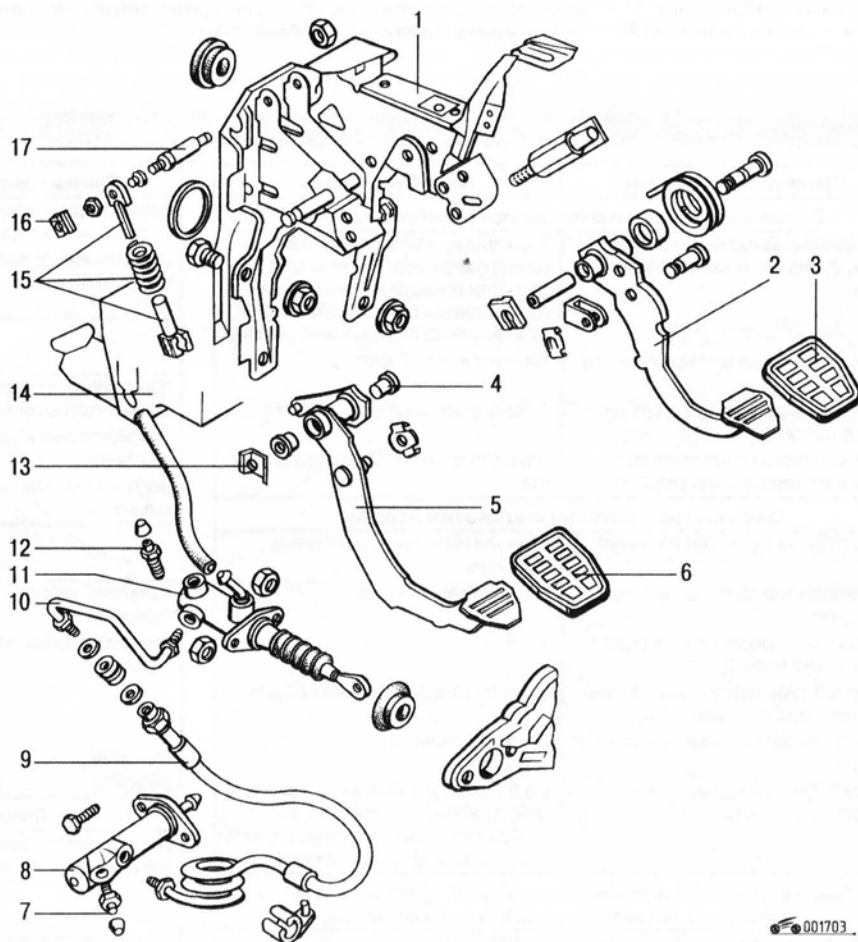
Педаль сцепления с гидравлическим приводом: 1 – кронштейн педали; 2 – педаль тормоза; 3, 6 – накладки педалей сцепления и тормоза; 4 – втулка; 5 – педаль сцепления; 7 – штуцер прокачки рабочего цилиндра сцепления; 8 – рабочий цилиндр сцепления; 9 – гибкий шланг; 10 – трубопровод; 11 – главный цилиндр сцепления; 12 – штуцер прокачки главного цилиндра сцепления; 13 – пружинный фиксатор; 14 – бачок гидравлического привода выключения сцепления/главного тормозного цилиндра; 15 – сервомеханизм; 16 – пружинный фиксатор; 17 – ось сервомеханизма
